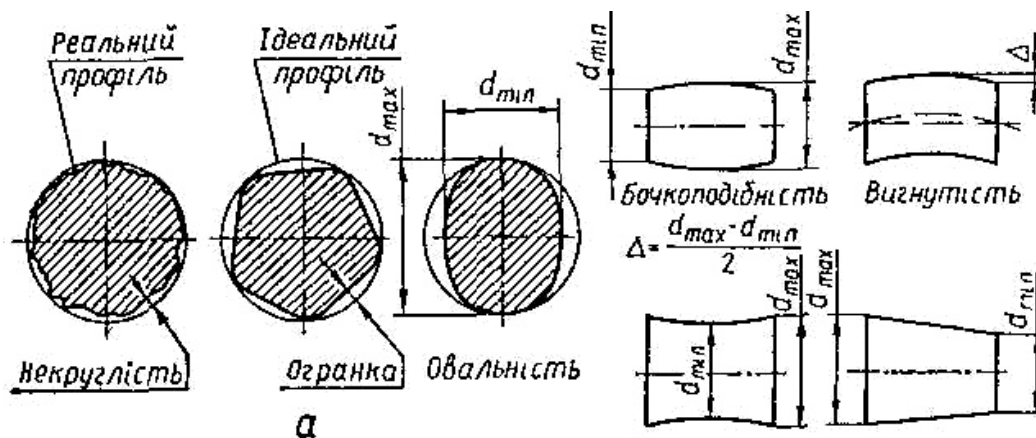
Відхилення форми деталей із циліндричними поверхнями
